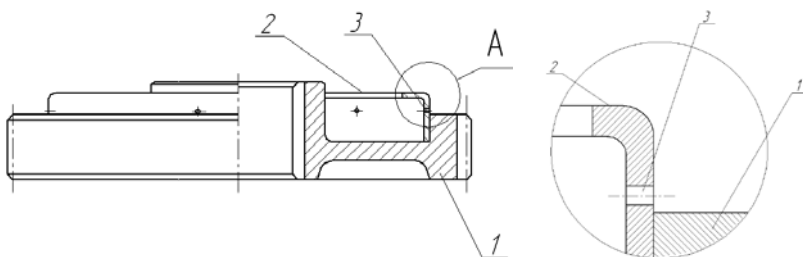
Шестерня с цилиндрической вставкой: 1 – шестерня;
